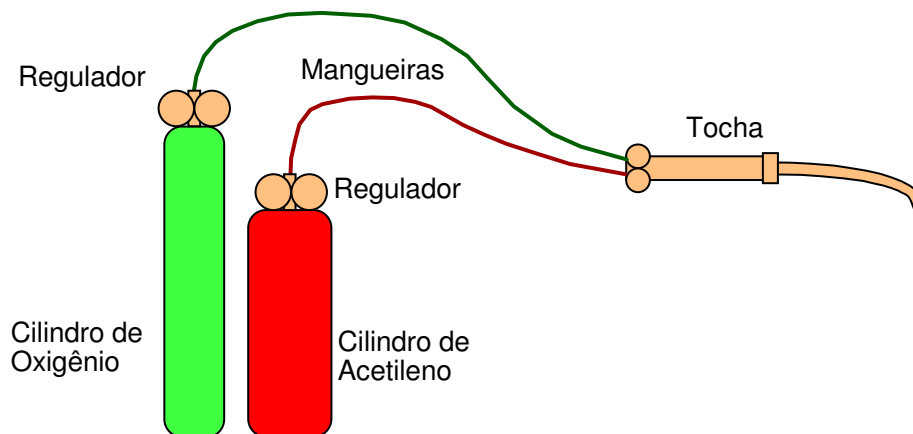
Equipamento para a soldagem oxi-acetilênica.
